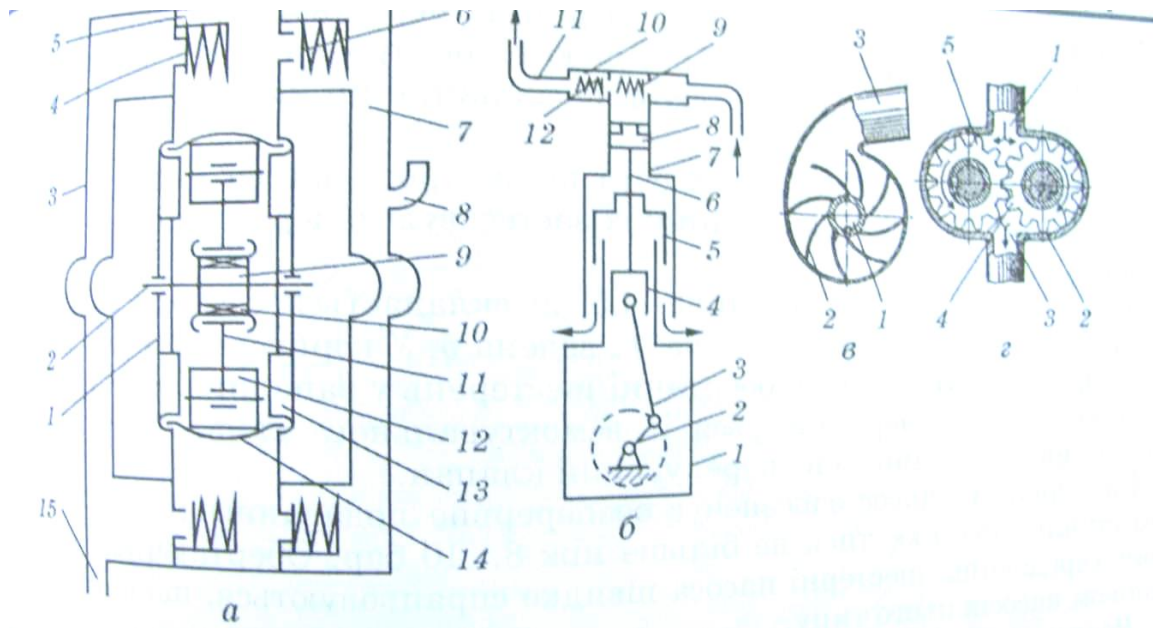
Схема роботи насосів: а — мембранно-поршневий: 1 — корпус; 2 — вал; 3 — всмоктувальний колектор; 4 — всмоктувальний клапан; 5 — кришка; 6 — нагнітальний клапан; 7 — нагнітальний колектор; 8 — нагнітальний канал; 9 — эксцентрик; 10 — голчастий підшипник; 11 — шатун; 12 — поршень; 13 — циліндр; 14 — мембрана; 15 — вхідний канал; б — трипоршневий: 1 — корпус насоса; 2 — колінчастий вал; 3 — шатун; 4 — повзун; 5 — захисний екран; 6 — шток; 7 — циліндр; 8 — поршень; 9 — всмоктувальний клапан; 10 — клапанна коробка; 11 — нагнітальна магістраль; 12 — нагнітальний клапан; в — відцентрований насос: 1 — всмоктувальний канал; 2 — робоче колесо; 3 — напірний канал; г — шестеренний насос: 1 — всмоктувальний канал; 2 — корпус; 3 — напірний канал; 4 — ведуча шестірня; 5 — ведена шестірня
